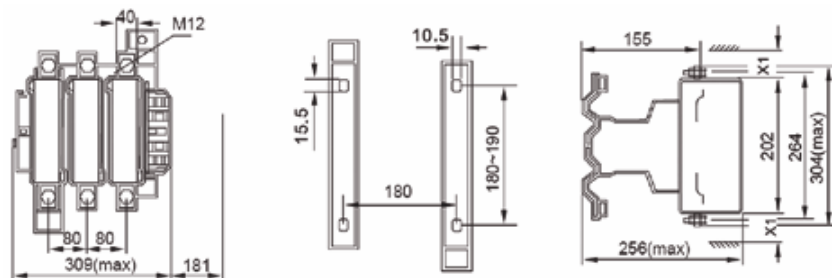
Габаритные и установочные размеры контакторов серии КМ-102 800А, мм.
